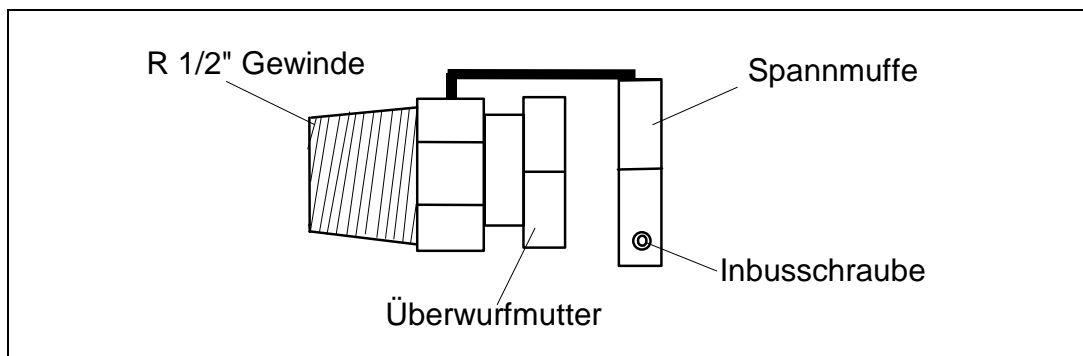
Klemmringverschraubung mit angeschweißter Spannmuffe
